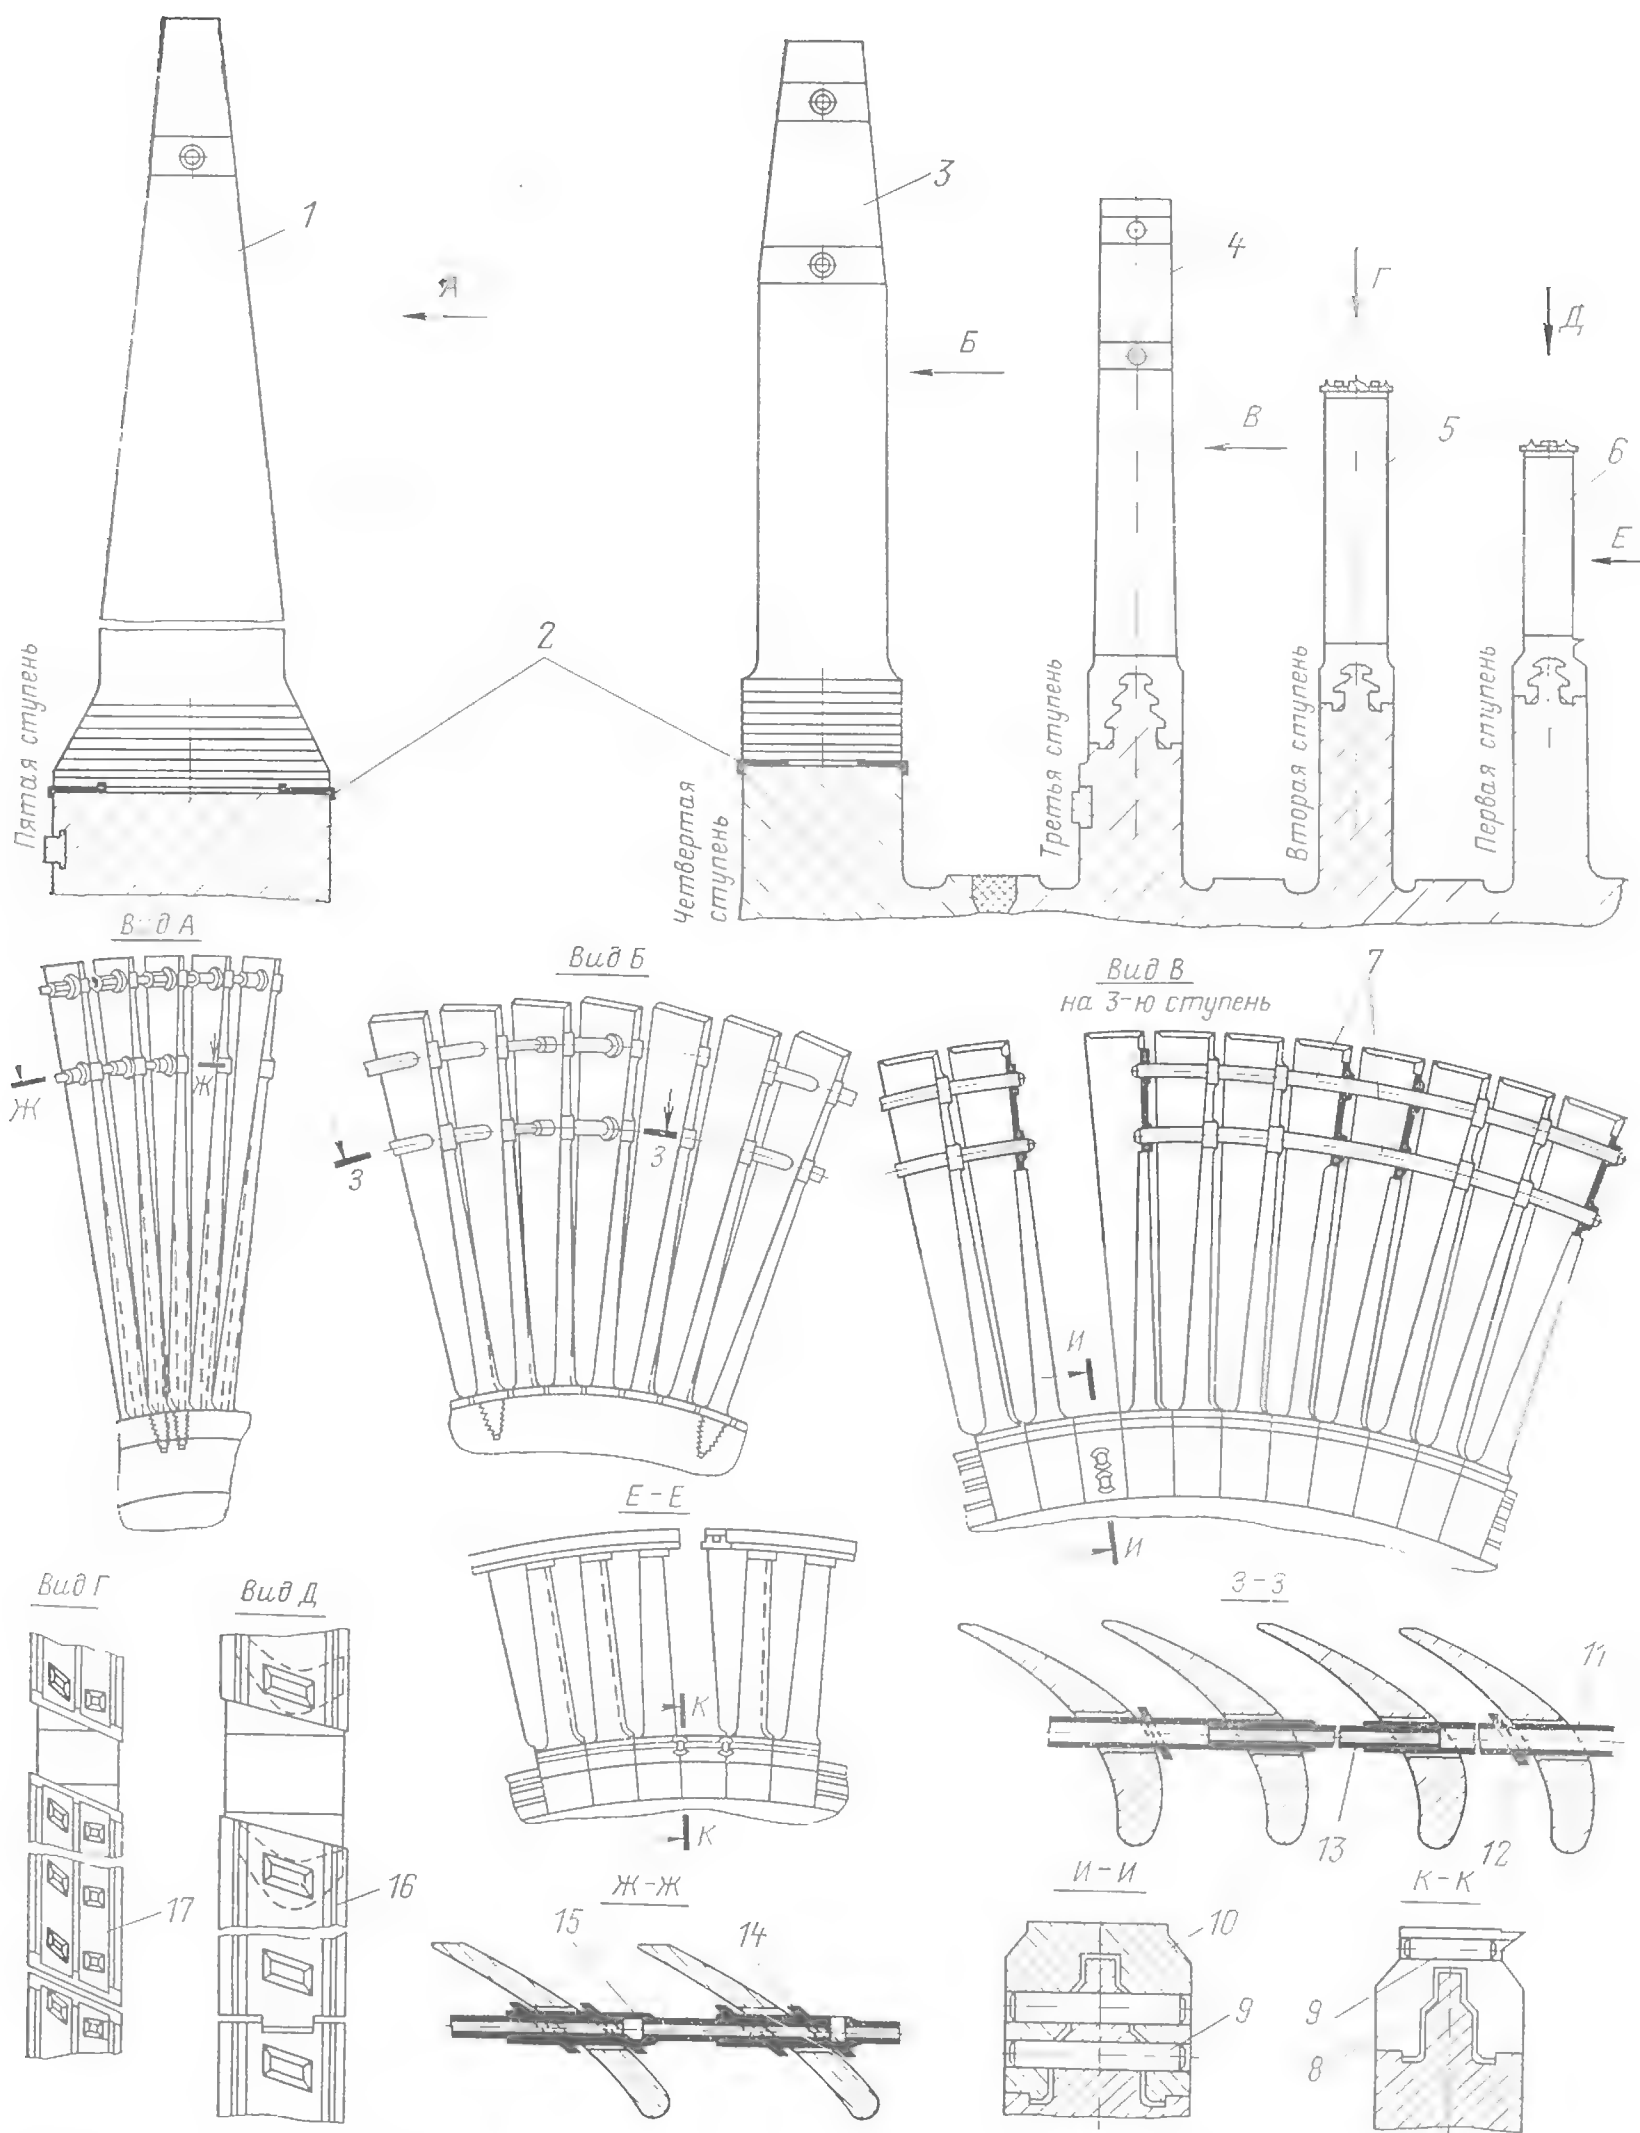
Рабочие лопатки ротора низкого давления турбины К-500-65/3000 ХТЗ:
